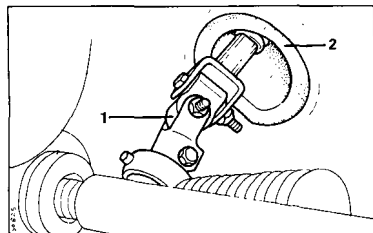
Универсальный шарнир между промежуточным валом и валом ведущей шестерни
